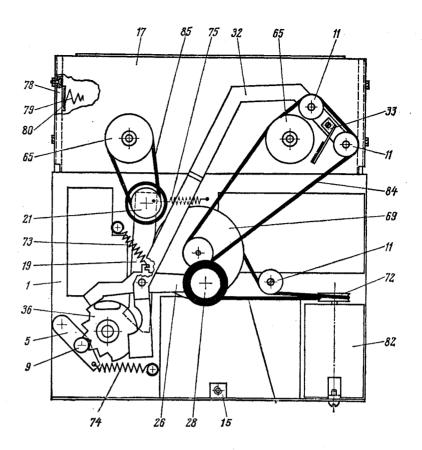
Сборочный чертеж лентопротяжного механизма: 1—шасси (передняя часть); 5—рычаг фиксатора;
